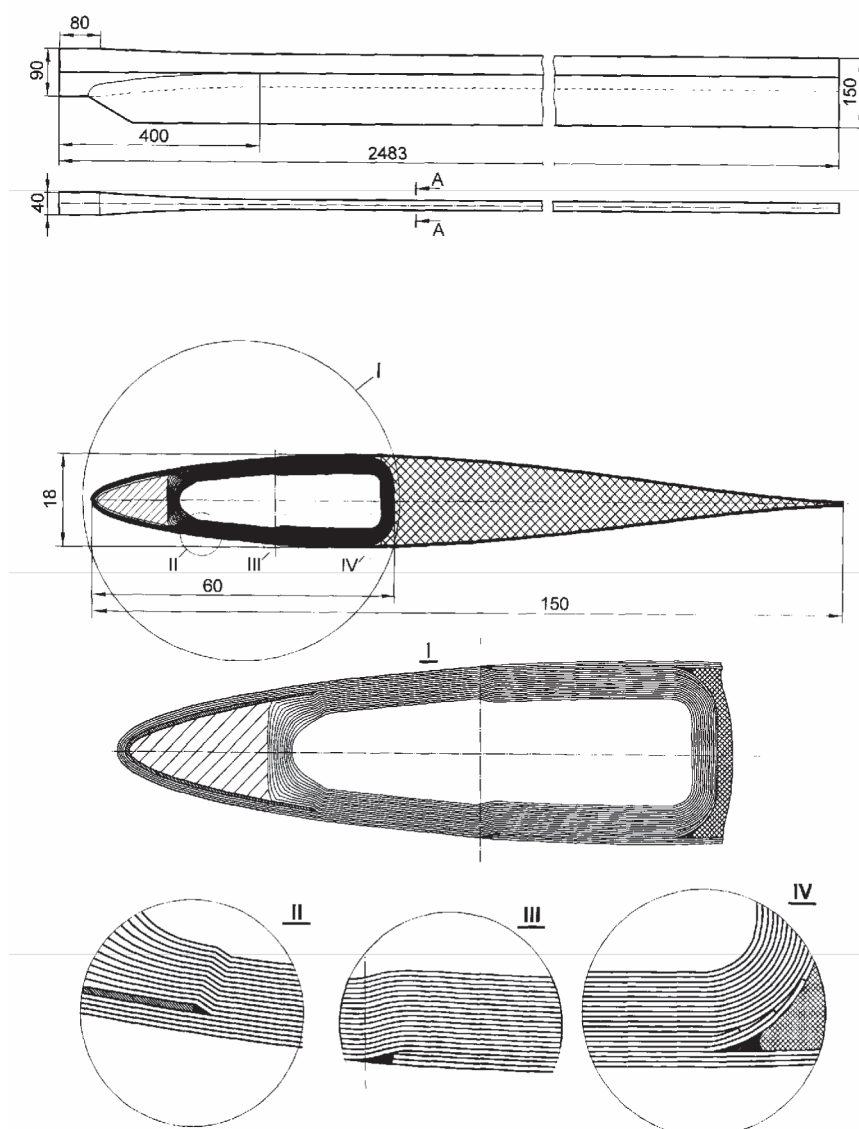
Общий вид конструкции лопасти несущего винта вертолета
